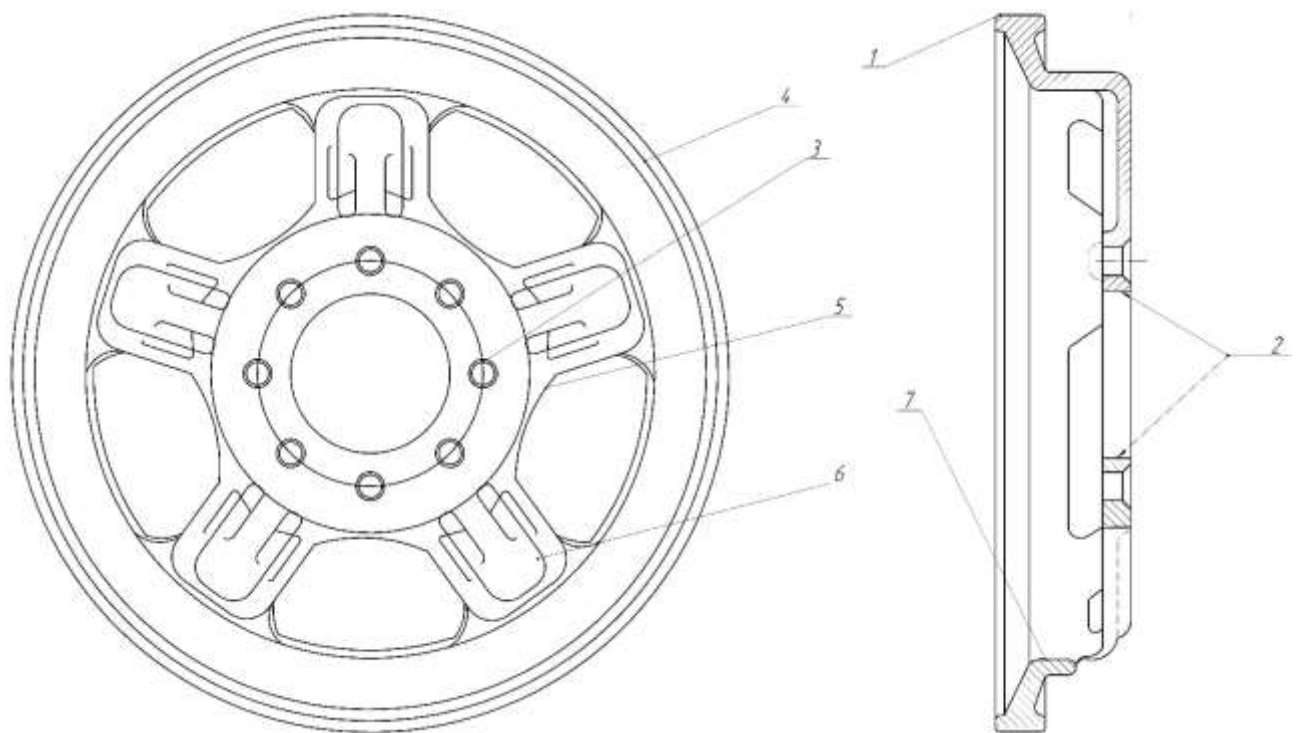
Ескіз з вказаними номерами поверхонь
